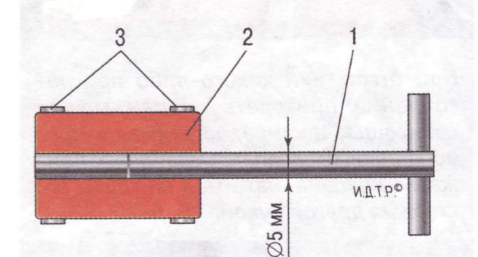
Приспособление для притирки клапанов: 1 – металлический стержень; 2 – резиновый шланг; 3 – винтовой хомут
